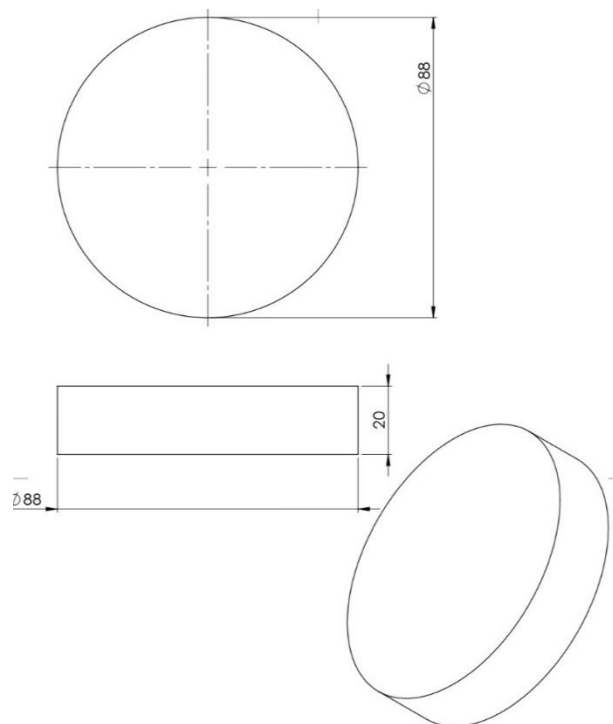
Desenho técnico da peça tampa do conjunto de prensagem.
